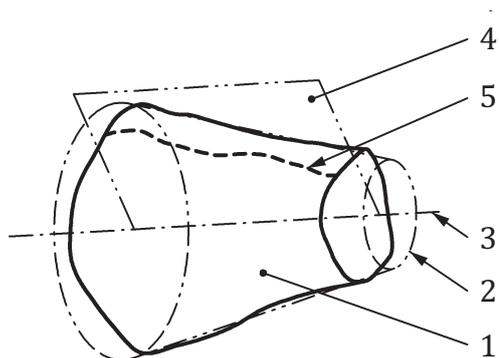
Exemple de plan d'intersection utilisé pour établir un élément tolérancé élémentaire
